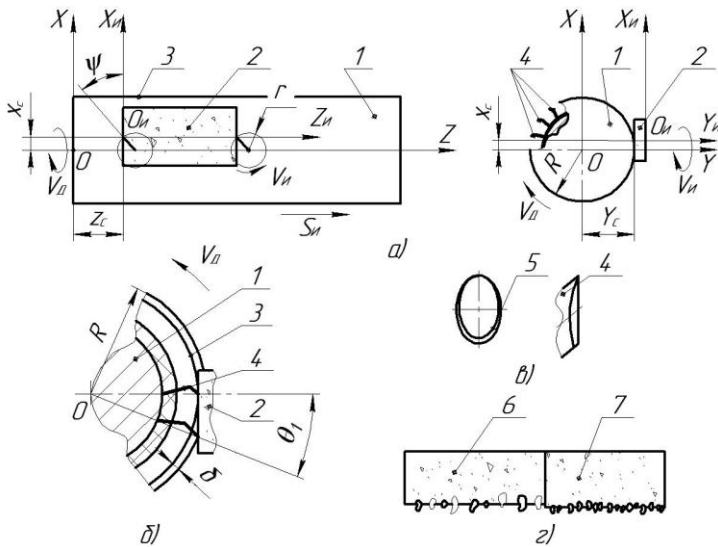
Схема обробки циліндричної голчастої поверхні торцем бруска
